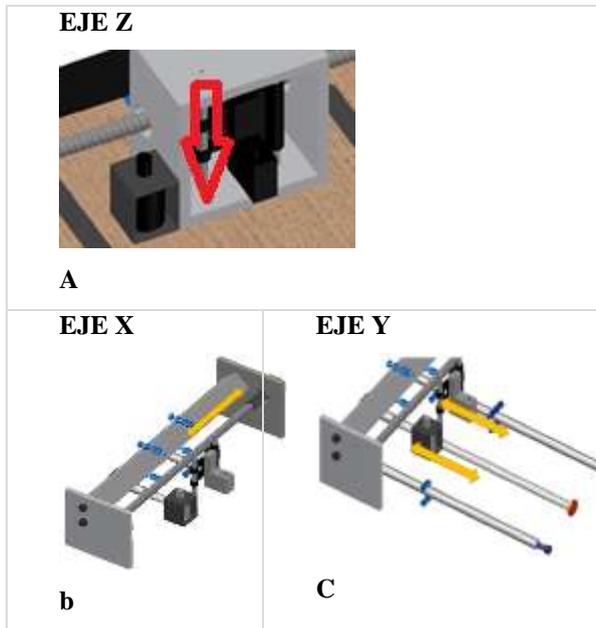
Diseño de conjunto de Ejes y tornillo sin fin .
